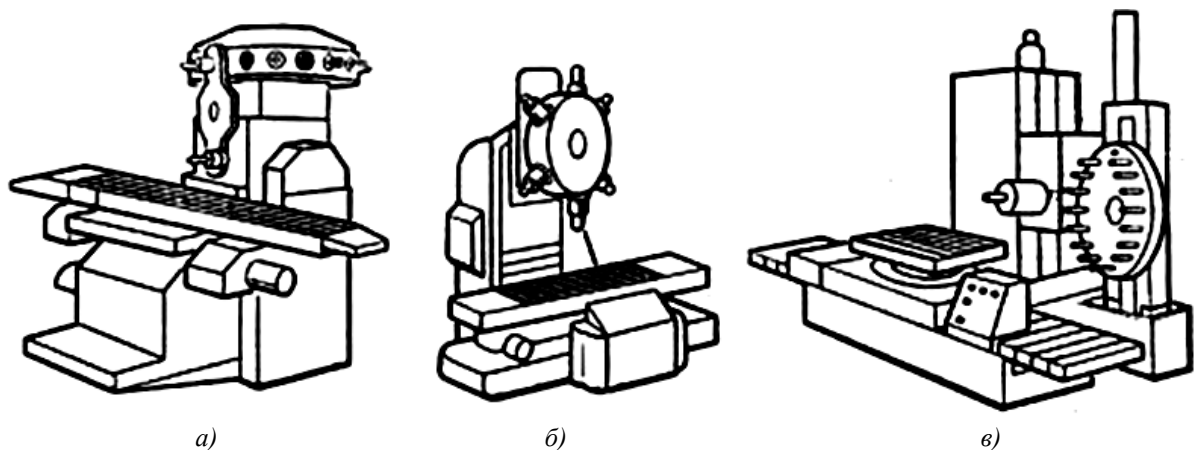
Варіанти конструкції верстата, створеного за модульним принципом для обробки корпусних деталей (3 керовані координати)
